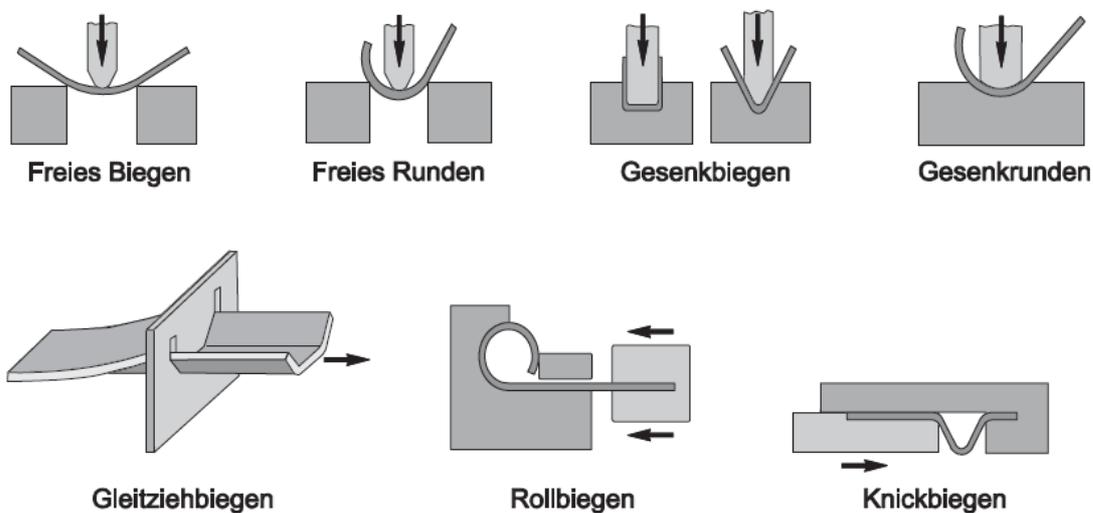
Das Biegeumformen mit geradliniger Werkzeugbewegung ^[2]
